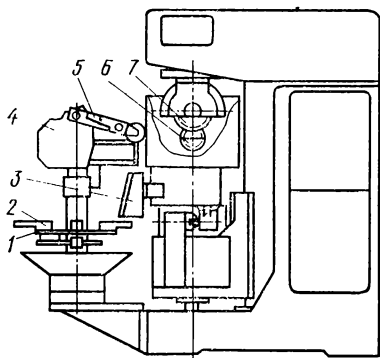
Зубошевинговальный автомат мод. АВС-02В-1774
